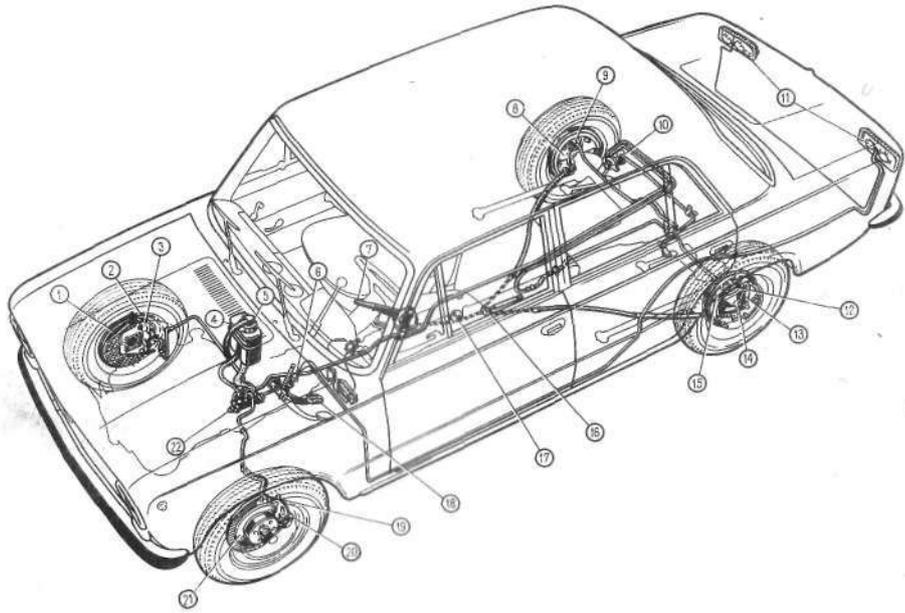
Схема тормозной системы: 1 — защитный кожух переднего тормоза; 2 и 19 — трубопроводы соединения двух гидроцилиндров суппорта тормозов; 3 — суппорт переднего тормоза; 4 — бачок для жидкости привода тормозов; 5 — крышка бачка с сигнализатором недостаточного уровня тормозной жидкости; 6 — выключатель стоп-сигнала; 7 — рычаг стояночного тормоза; 8 — щит барабанного тормоза; 9 — штуцер для прокачки гидравлической системы задних тормозов; 10 — регулятор интенсивности торможения, действующий на гидравлический привод задних тормозов; 11 — стоп-сигнал; 12 — рабочий цилиндр заднего тормоза; 13 — рычаг ручного привода колодок тормоза; 14 — разжимная планка; 15 — колодки задних тормозов с фрикционными накладками; 16 — уравниватель заднего троса привода стояночного тормоза; 17 — направляющий ролик привода стояночного тормоза; 18 — педаль тормоза; 20 — штуцер для прокачки гидравлической системы передних тормозов; 21 — тормозной диск; 22 — главный цилиндр гидросистемы тормозов
